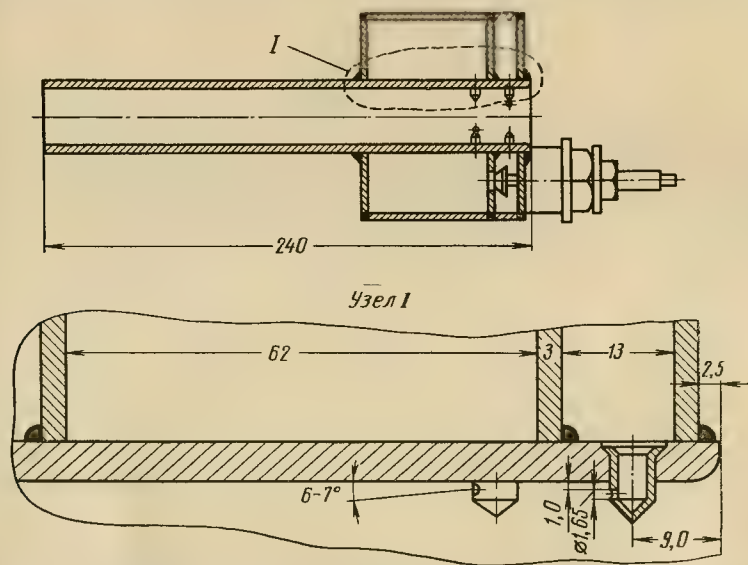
Щелевая одноканальная горелка сварной конструкции с периферийной подачей газа.
